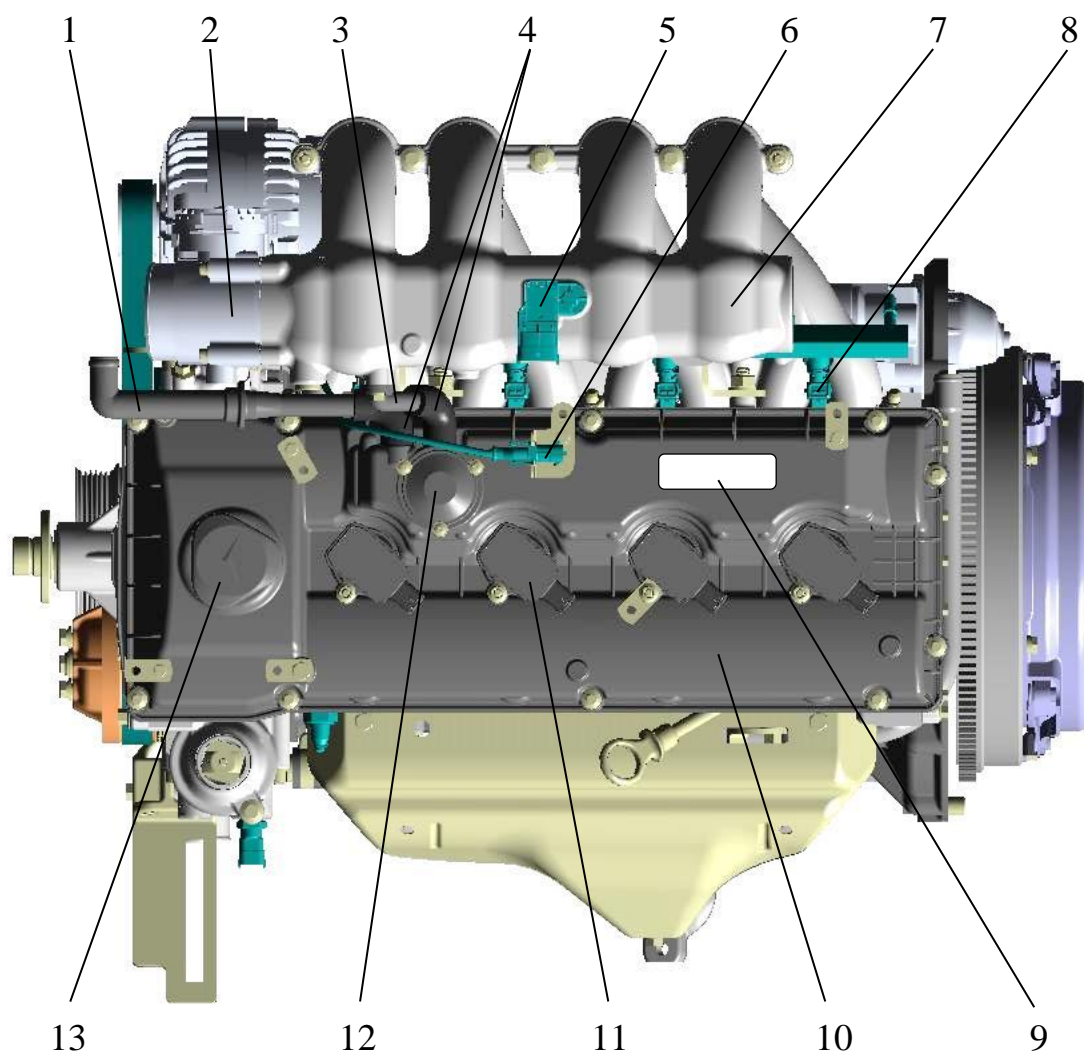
Вид сверху двигателя ЗМЗ-40905.10:
